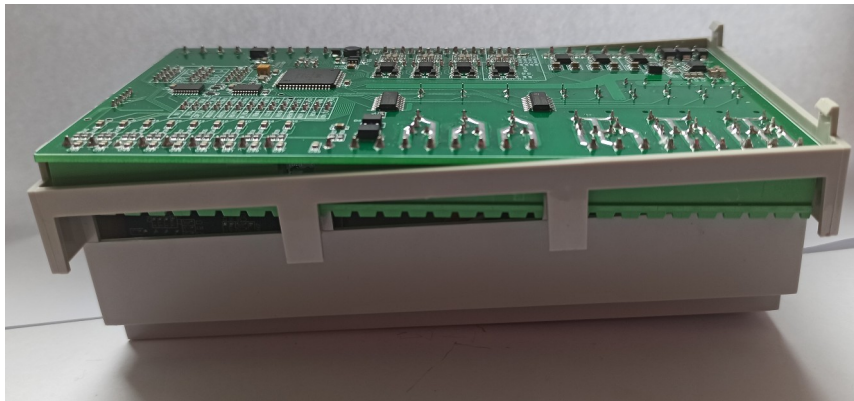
Вставлення плати BASE в корпус (вид знизу)
